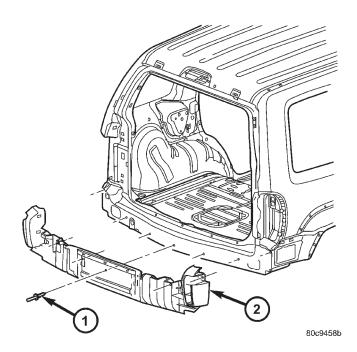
SOPORTE DE LA PLACA PROTECTORA TRASERA
